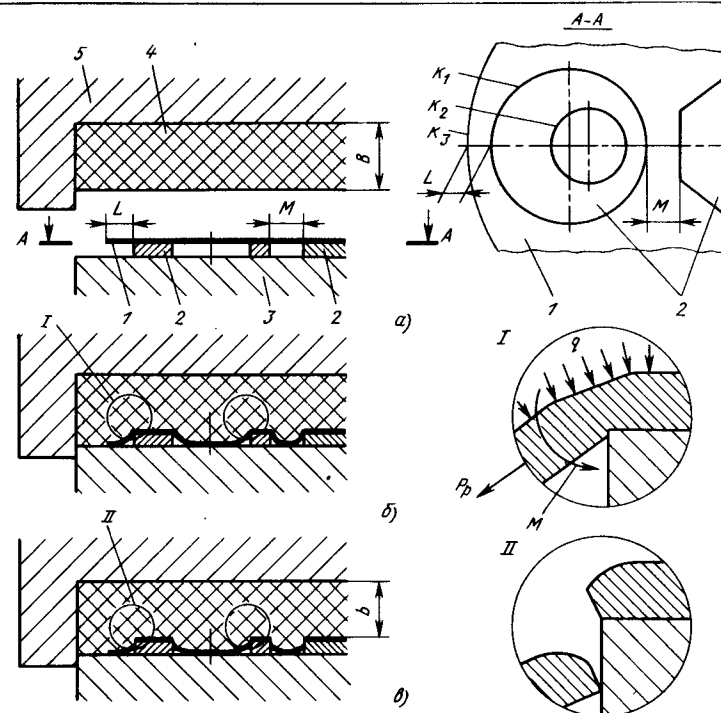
Схема вырубki и пробивки в штампе с эластичной средой:
